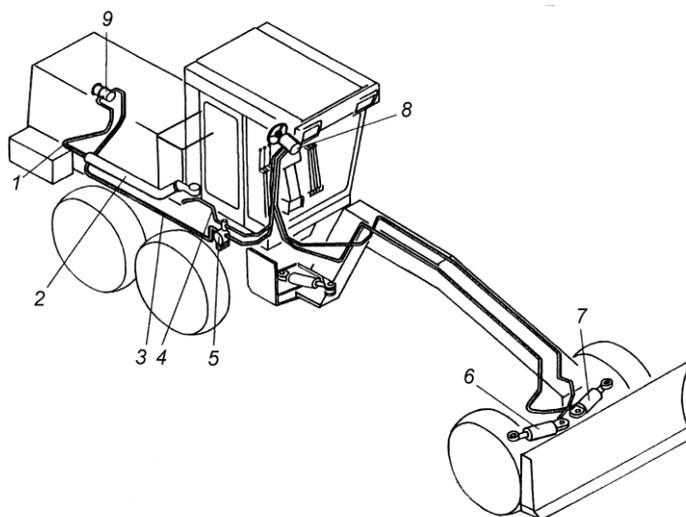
Рулевое управление автогрейдера А120: 1 – рукав всасывания; 2 – заборная труба; 3 – напорная гидрочиния; 4 – рукав слива; 5 – предохранительный клапан; 6, 7 – гидроцилиндры; 8 – гидроруль; 9 – насос
